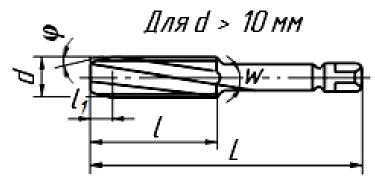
Метчик машинный из быстрорежущих сталей с винтовыми канавками (ГОСТ 17933–72)
